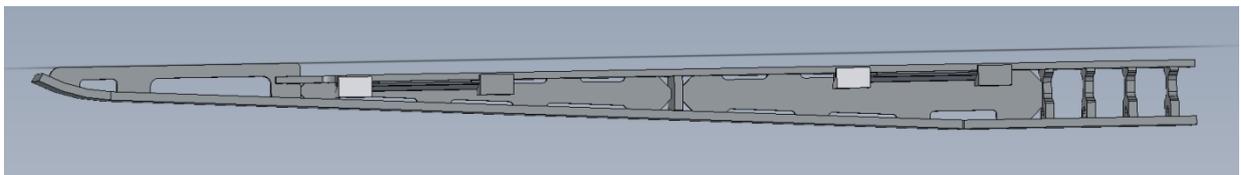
Ensamblaje Típico de Rampa (Previo a colocar cobertor)
